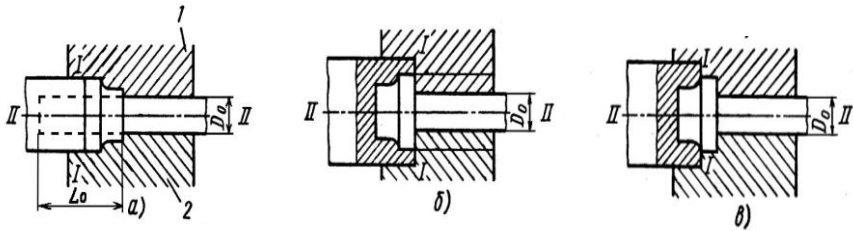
Схеми розташування поковки у штампах (горизонтальний розріз штампів, вигляд зверху):
